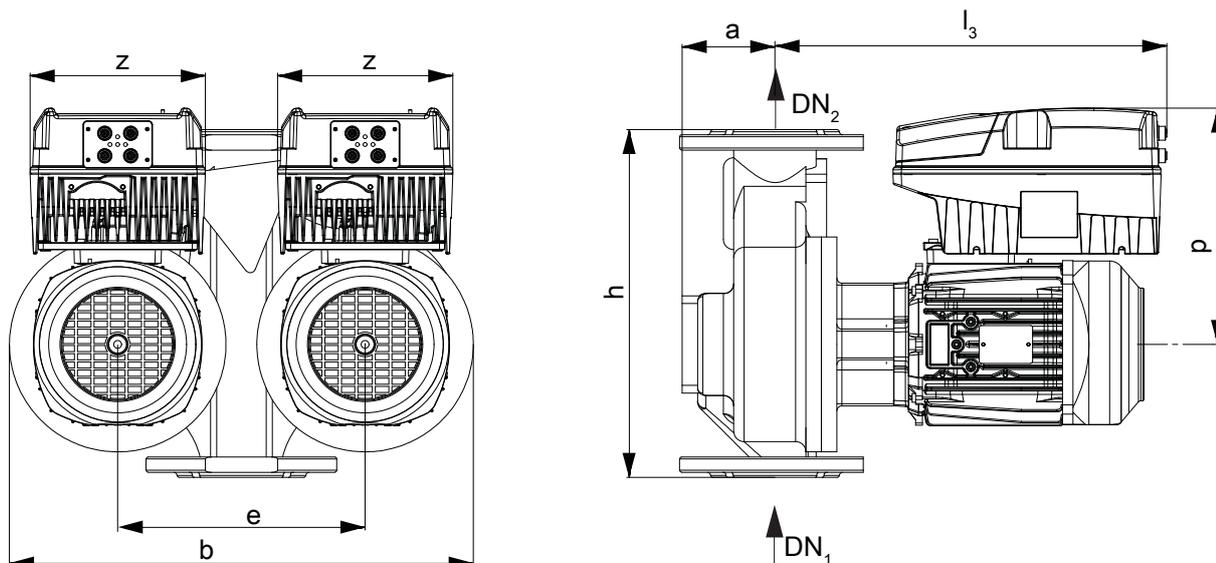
Dimensioni gruppo pompa con PumpDrive 2 Eco
